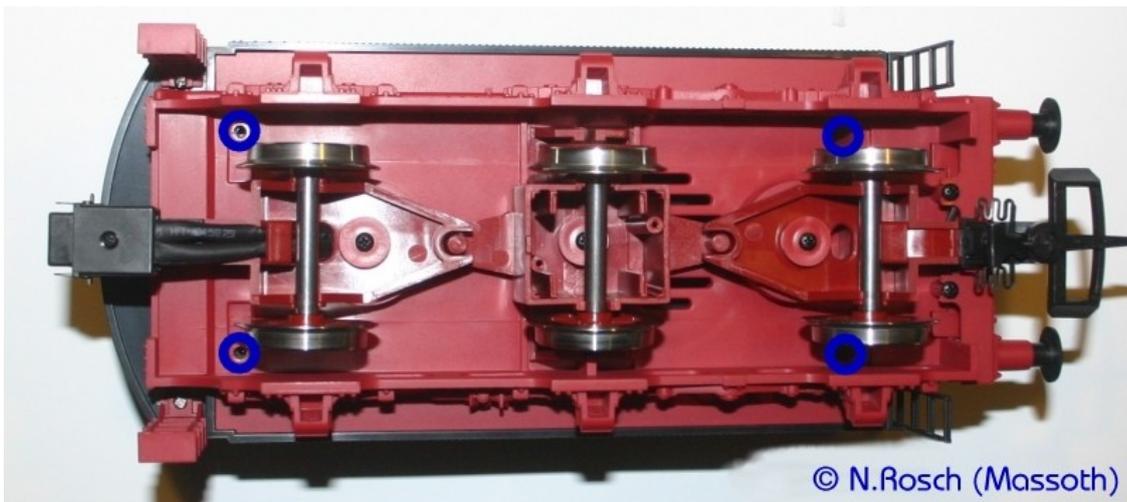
Entfernen der 4 Schrauben im Fahrzeugboden
